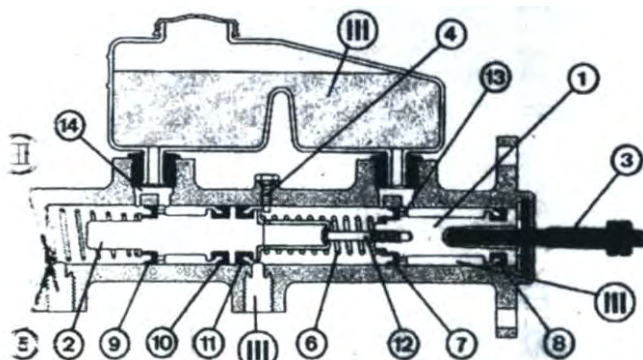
Исходное положение деталей главного тормозного цилиндра с последовательным расположением поршней, с перепускным отверстием: 1 – первый поршень; 2 – второй поршень; 3 – толкатель; 4 – ограничительный болт второго поршня; 5, 6 – возвратные пружины; 7, 8 – уплотнительные манжеты первого поршня; 9, 10 – уплотнительные манжеты второго поршня; 11 – изолирующая манжета между контурами привода тормозов; 12 – ограничительный болт первого поршня; 13 – компенсационное отверстие; 14 – перепускное отверстие
